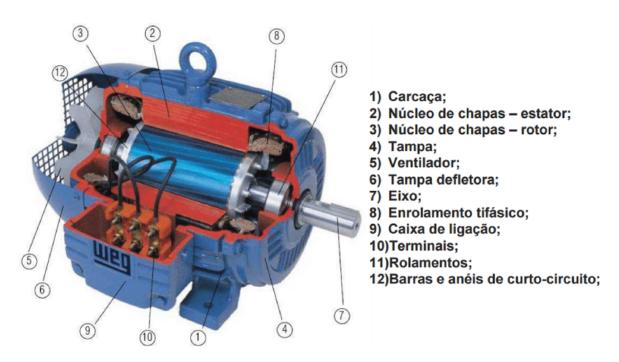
Destaque dos componentes do motor de indução trifásico em uma vista em corte. Fonte: WEG.
